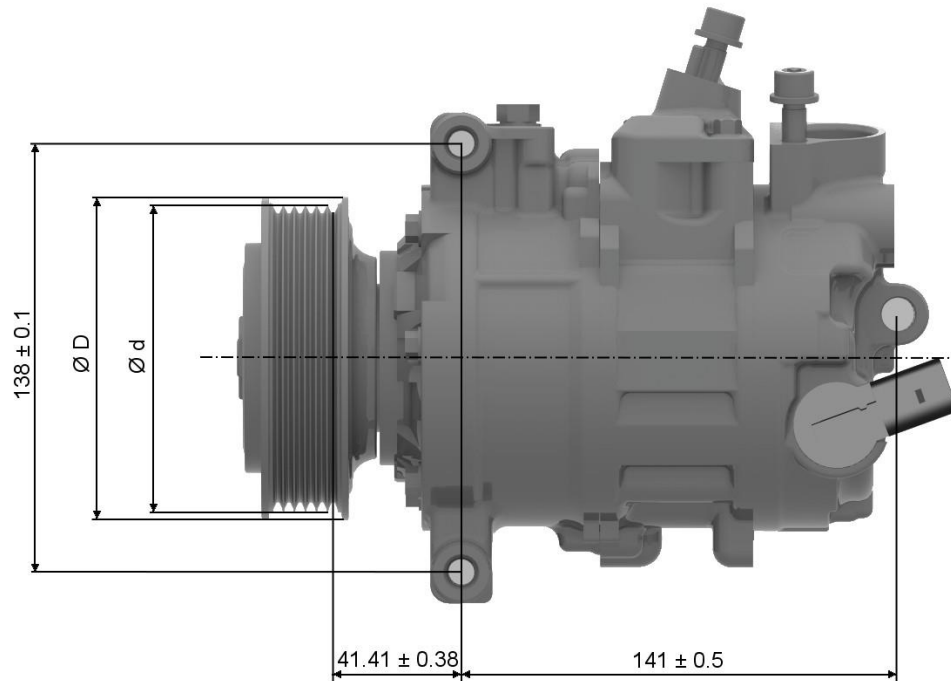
Размеры компрессора климатической установки, диаметр шкива – 110 мм (вид сбоку)
